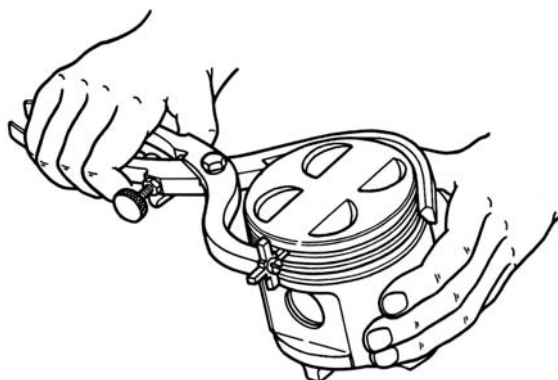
Очистка нагара в канавках поршней с помощью приспособления
